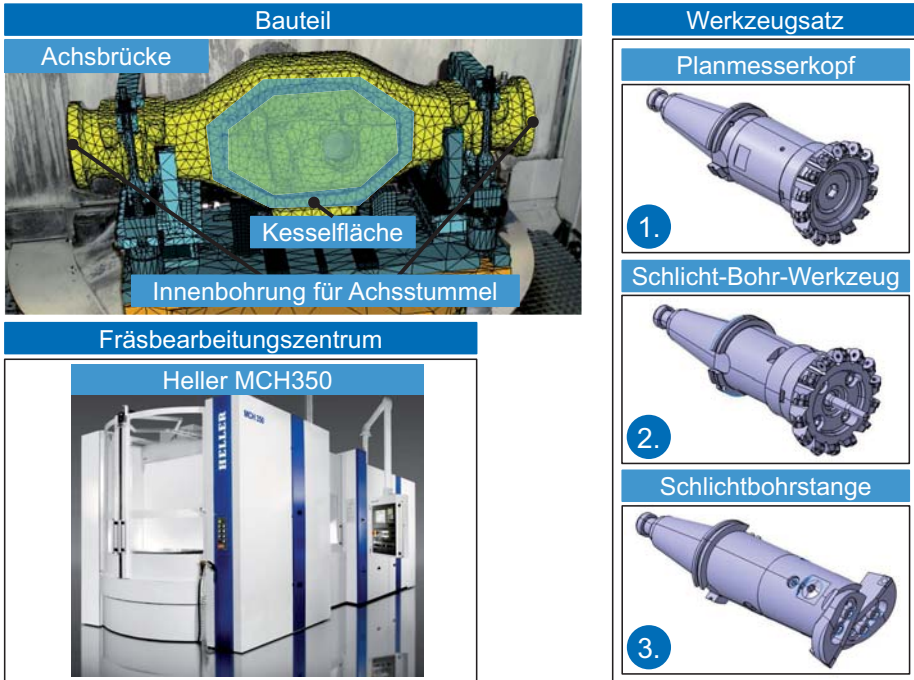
Validierungsszenario für die Fräsbearbeitung (MAN und Heller)
